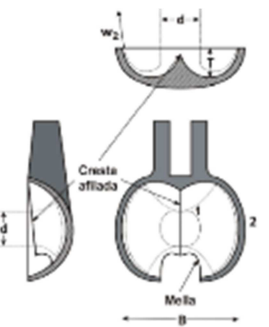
Vista frontal y sección lateral (izquierda) sección inferior de una cuchara
